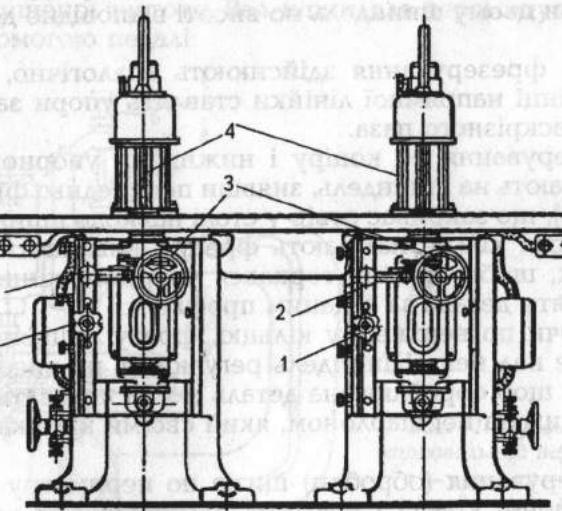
Двошпиндельний фрезерний верстат Ф2-4:
